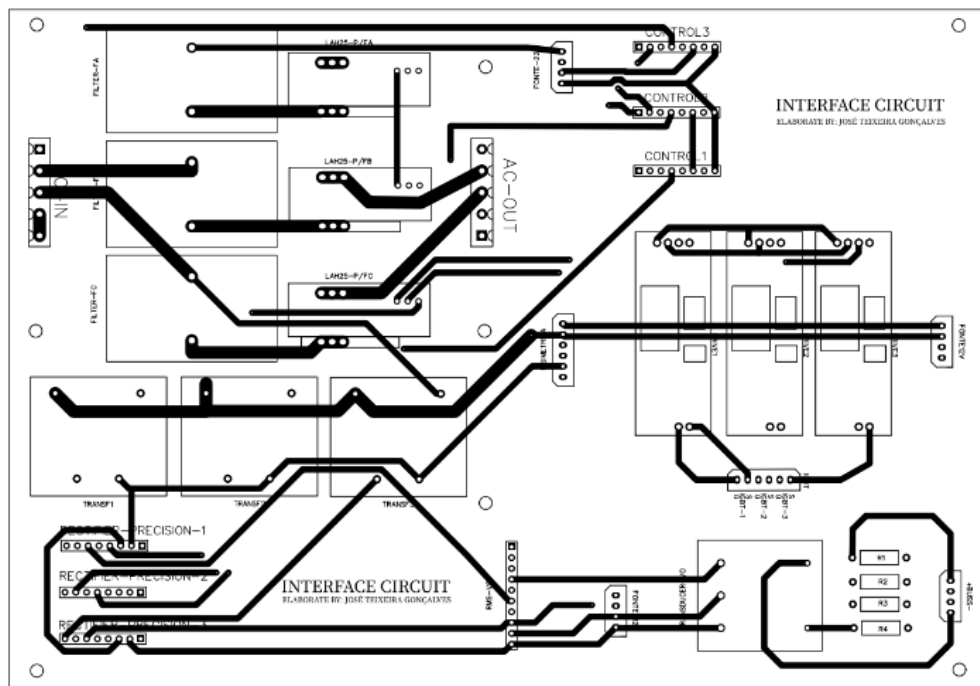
Placa PCB da camada superior do circuito de interface.
